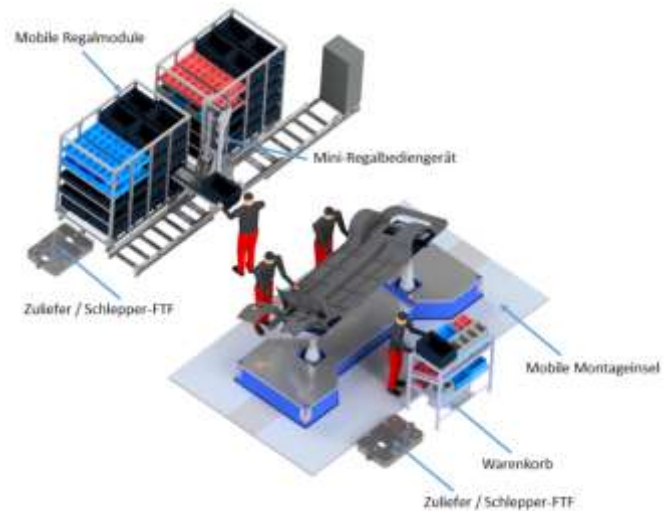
Materialzuführung zu einer mobilen Montageinsel mittels mobiler und semimobiler Komponenten [1], [2].
